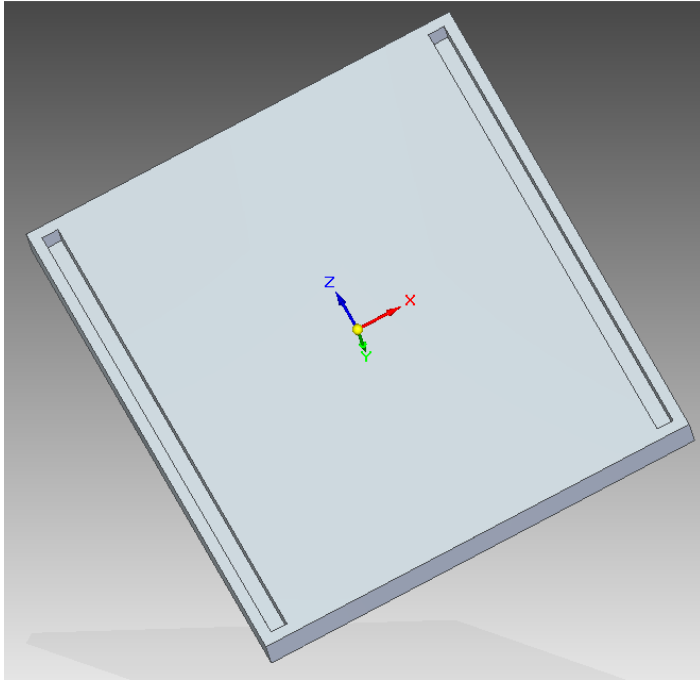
PARTE DE LA PUERTA TELESCÓPICA
